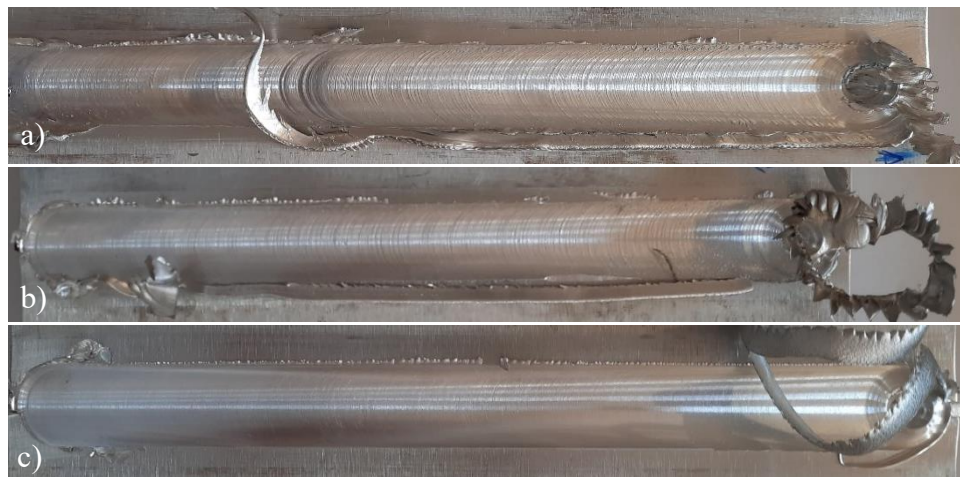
Aspeto superficial das soldaduras FSW de Mg: S-1500-90-7,1 (a), S-870-90-7,1 (b) e S-500-90-7,1 (c).
